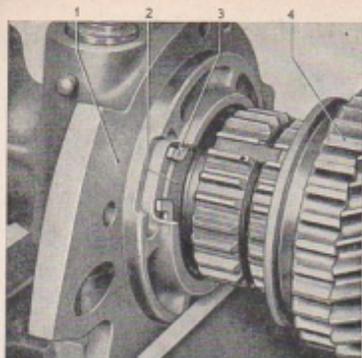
Sprengring für Kugellager in Getriebegehäuseverlängerung eingebaut
